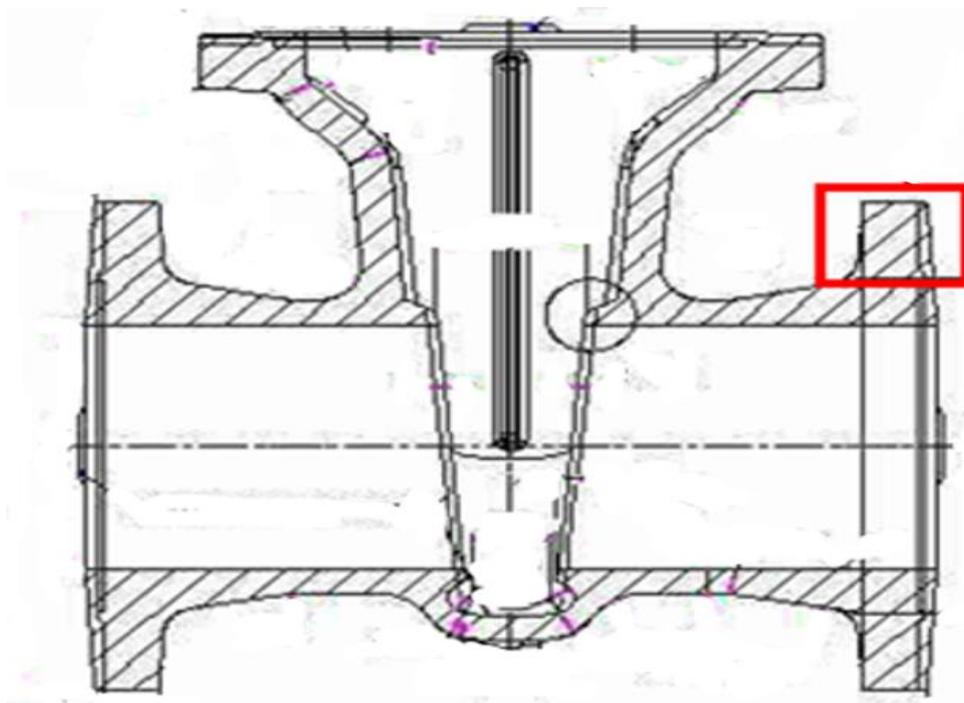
Схематичное изображение места отбора пробы для изготовления стандартного образца.
